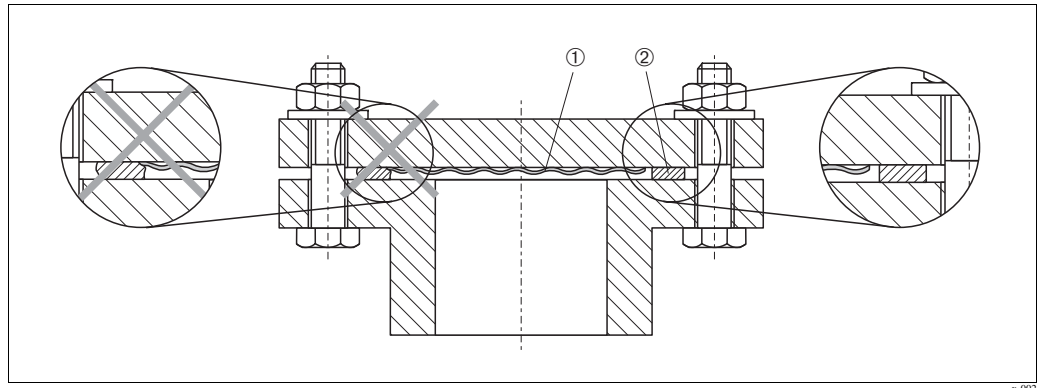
Montage der Versionen mit Flansch oder Druckmittler
